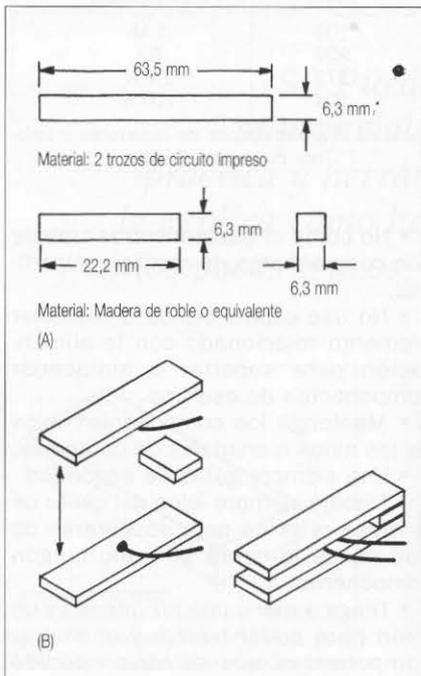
(A) Piezas para las pinzas de prueba para SMD. (B) Montaje del conjunto.
